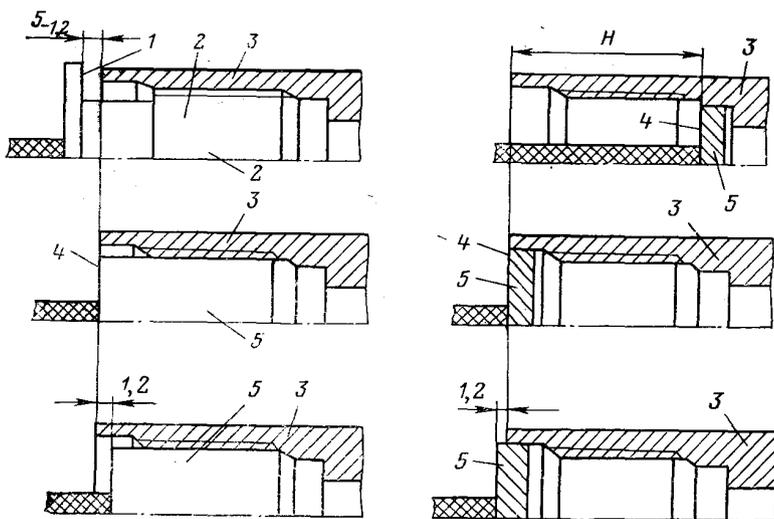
Контроль калибрами раструбного конца трубы резьбового соединения насосно-компрессорных труб НКБ:
